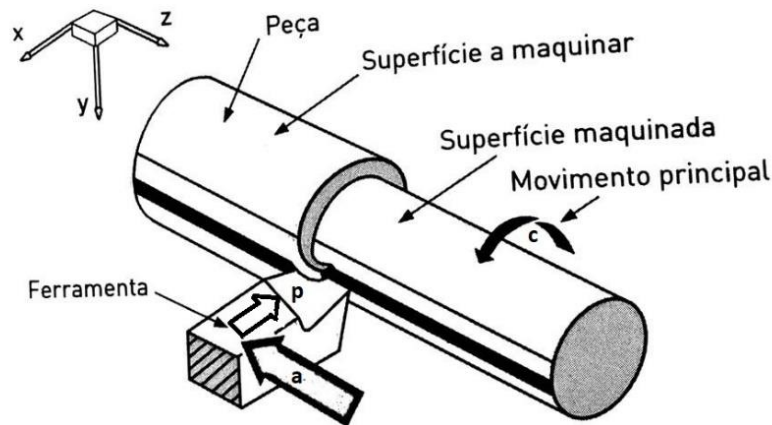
Operação de torneamento cilíndrico exterior [16]
